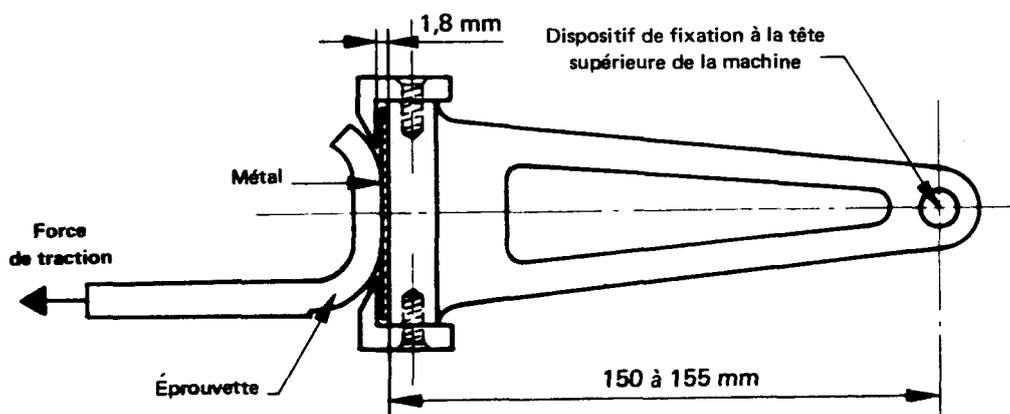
Dispositif de fixation pour l'essai d'adhérence
